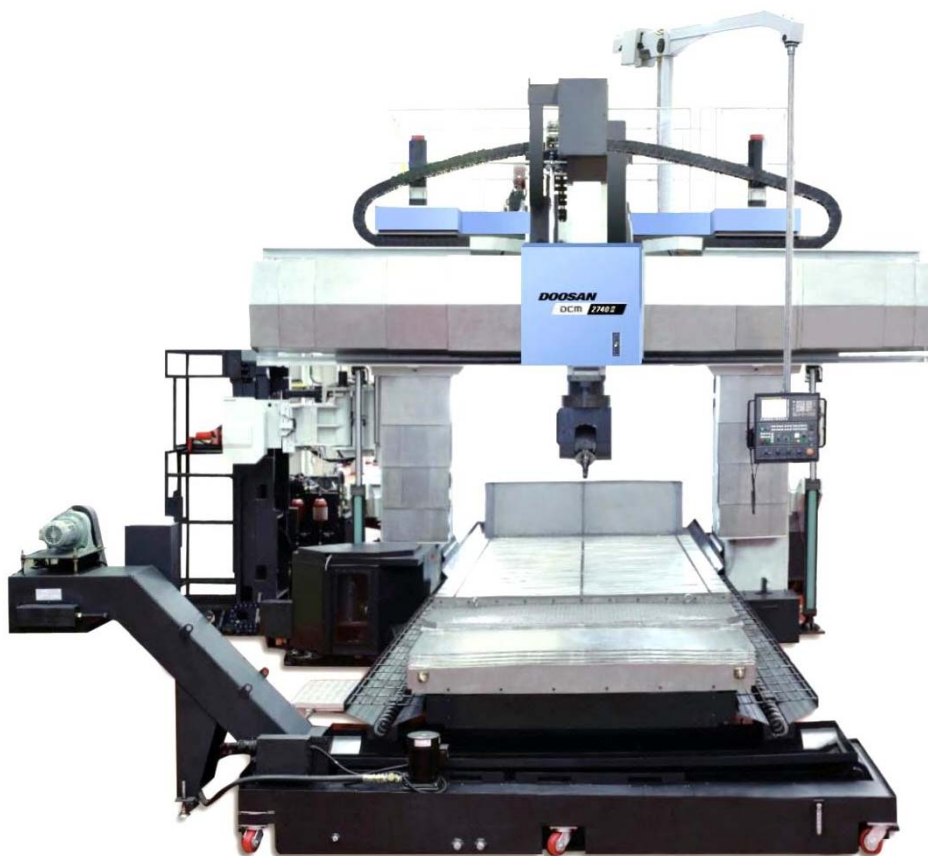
5-осевой обрабатывающий центр с двумя колоннами (портальный тип) модели DCM
